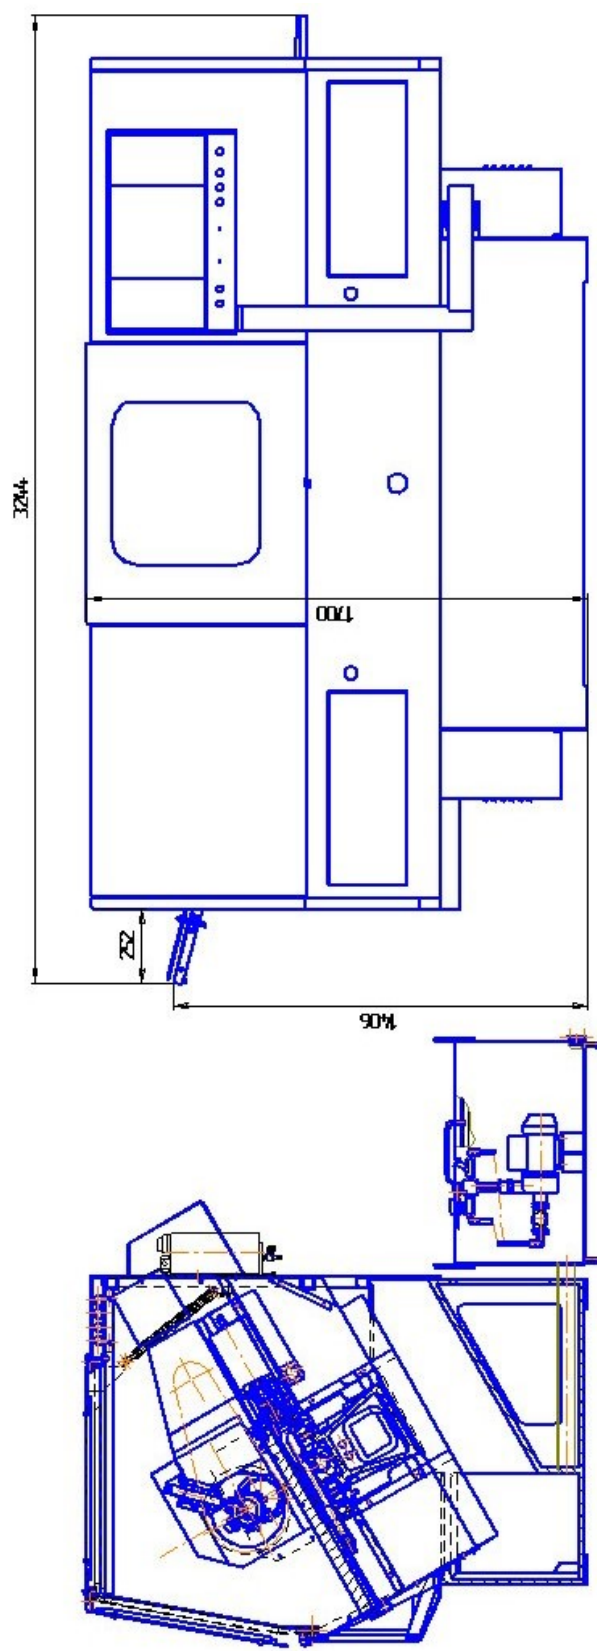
Загальний вигляд верстата з ЧПК з рухомою шпиндельною бабкою
